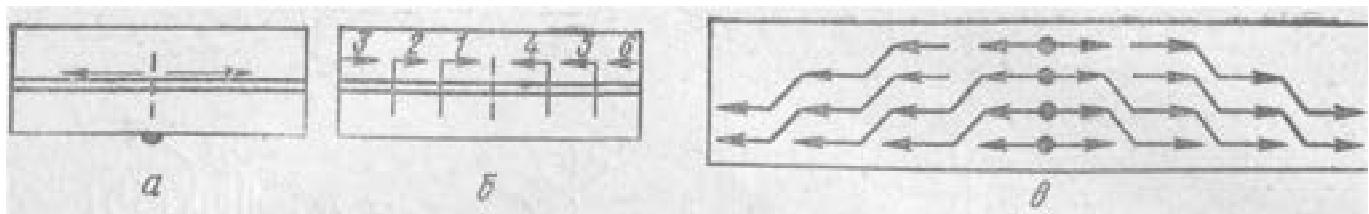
Ремонт сваркой (предотвращение коробления и образования внутренних напряжений):
